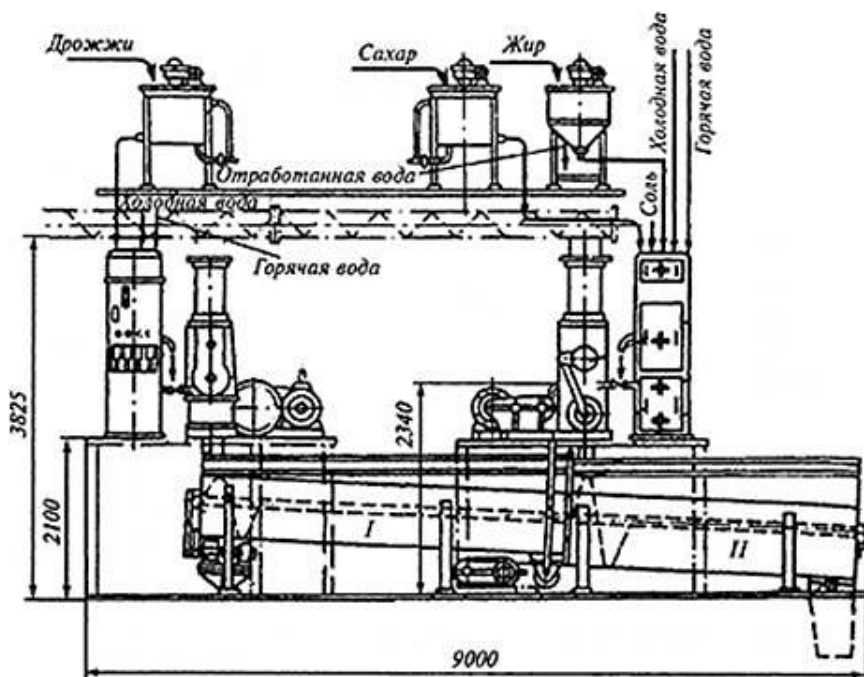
Схема тестоприготовительного агрегата марки ХТР:
